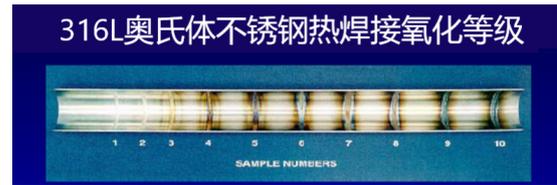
316L 奥氏体不锈钢热焊接氧化等级
